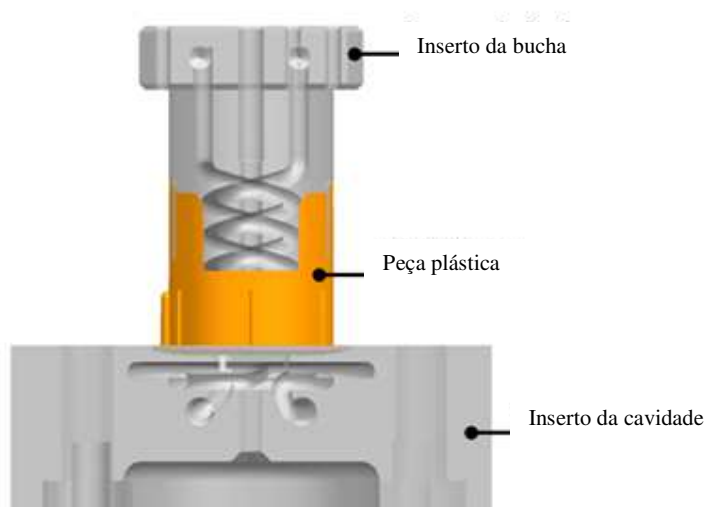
Zonas moldantes do molde de fabrico aditivo, *Sensor housing
